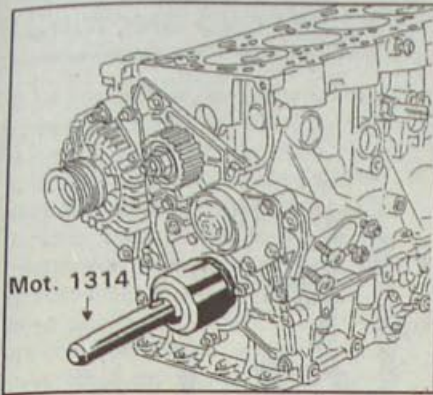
Использование приспособления Renault Mot. 1313 для установки переднего сальника коленчатого вала
